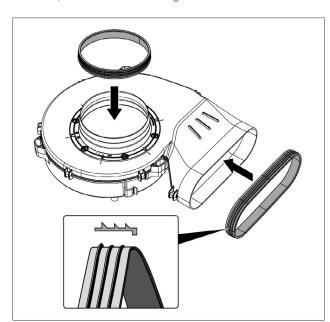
Colocar vedantes no ventilador de rodapé
